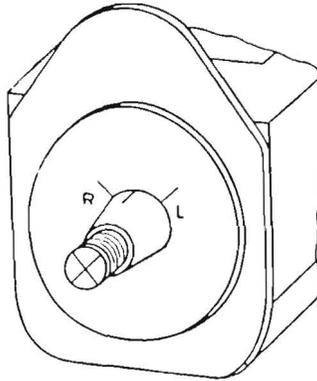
Richtiges Einstellen der Einspritzpumpe zum Motor
